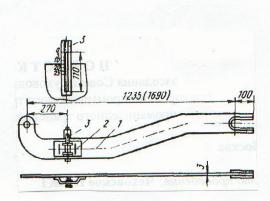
Шаблон для замера перехода длинного рычага через «мертвую точку»: 1 - рычаг; 2 - коробка; 3 - линейка.
